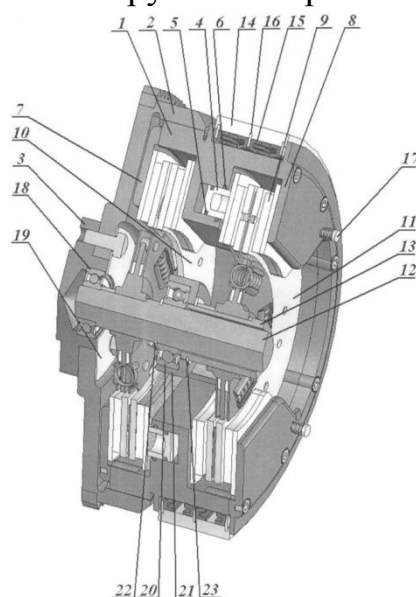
двухпоточной муфты сцепления в разрезе
